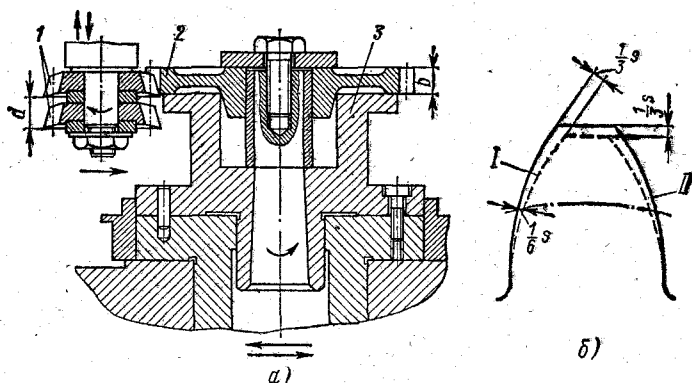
Нарезание зубчатого колеса двумя долбяками:
